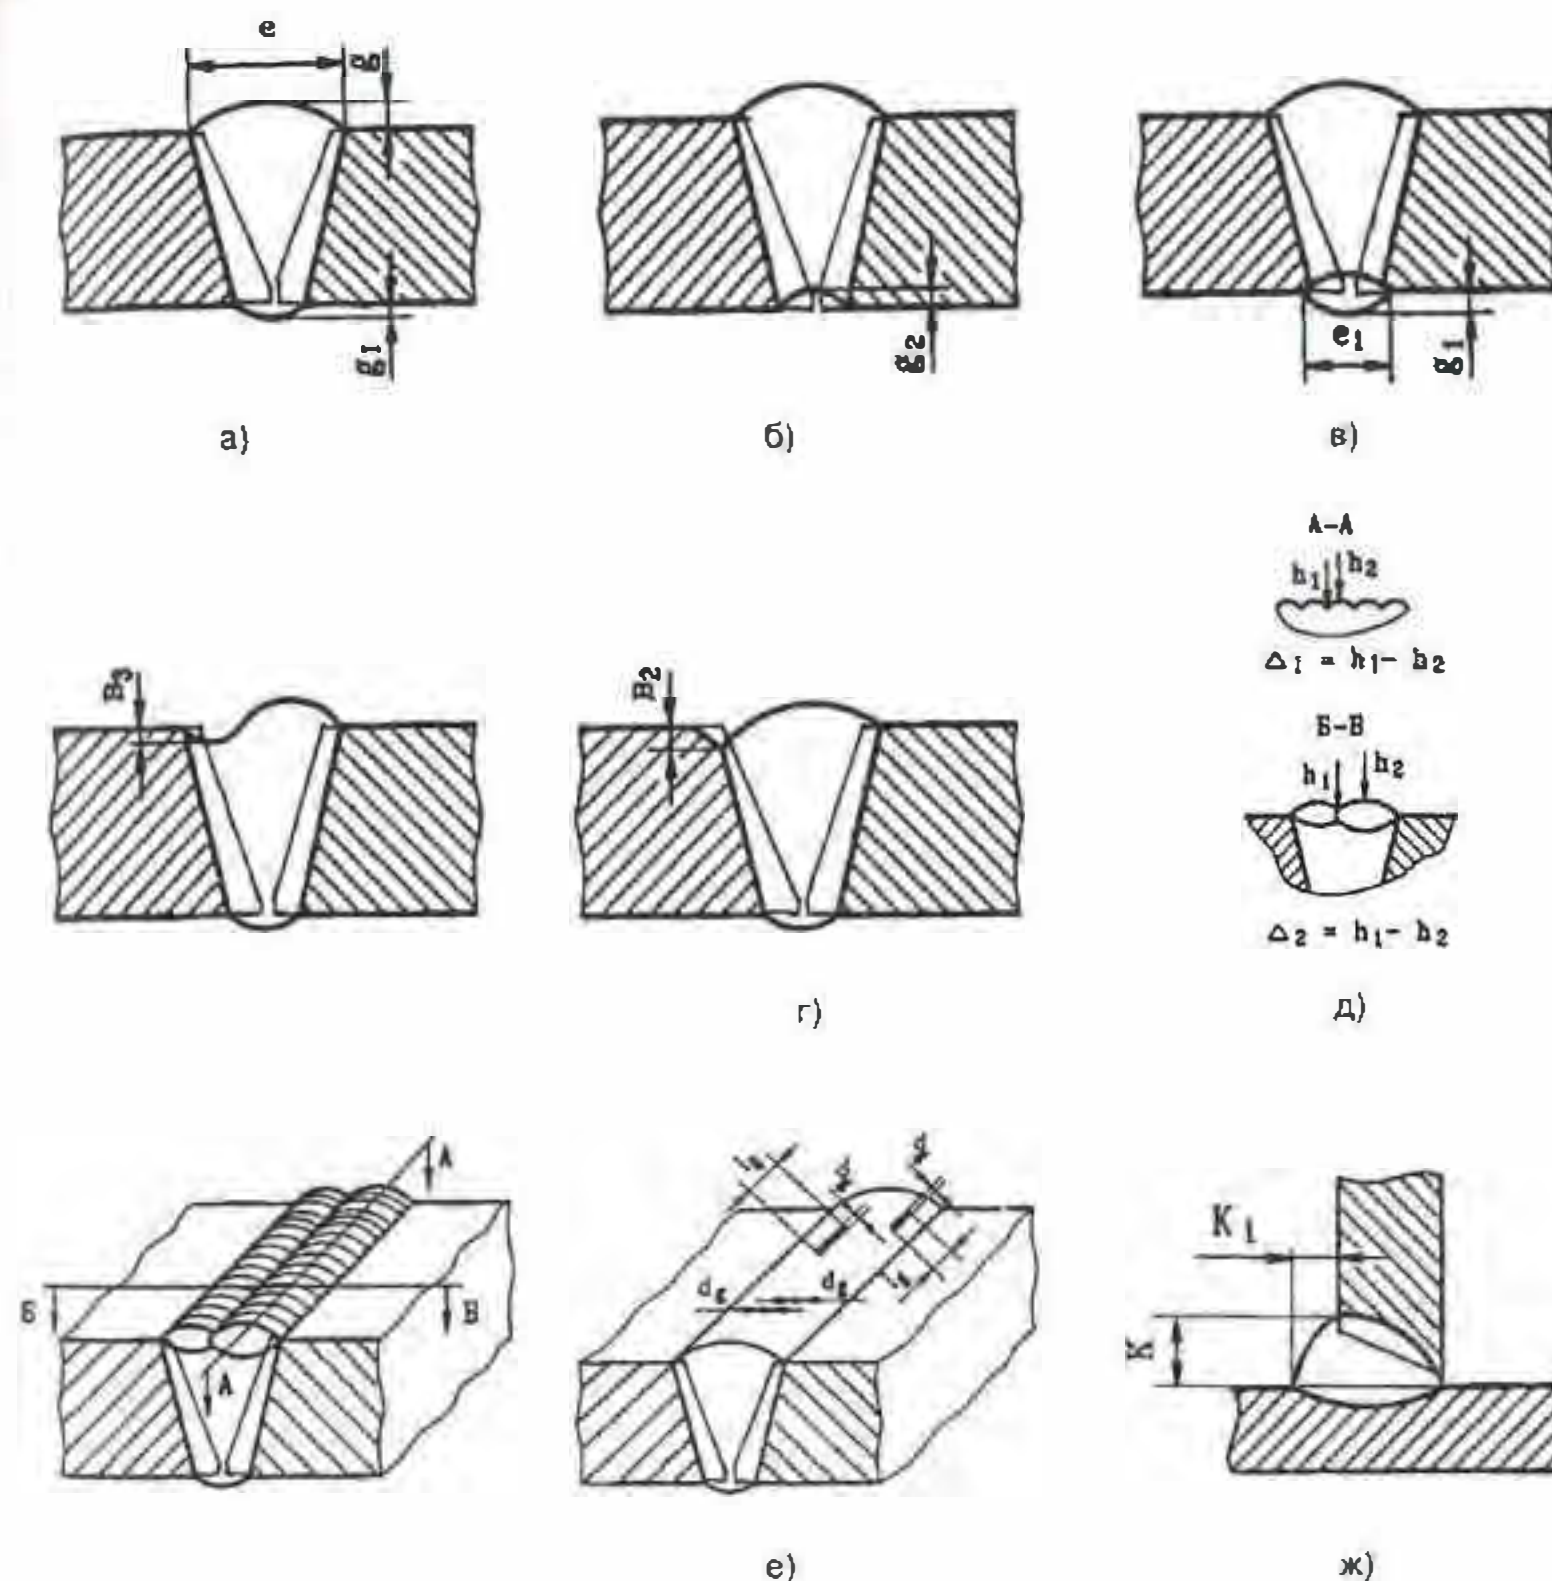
Конструктивные элементы и дефекты сварного шва, подлежащие измерительному контролю
